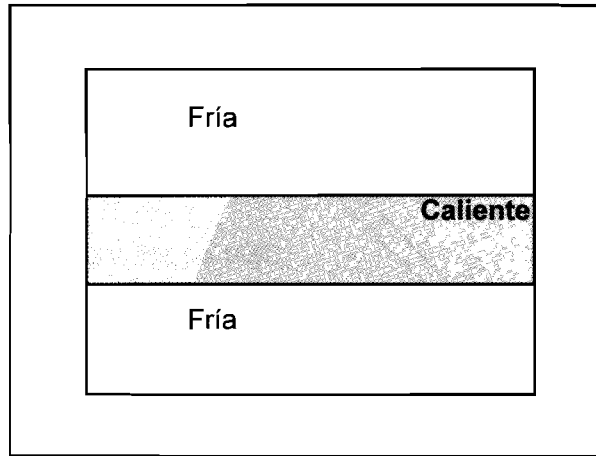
CALENTAMIENTO LOCAL PRODUCIDO DURANTE EL SOLDEO DE DOS CHAPAS
